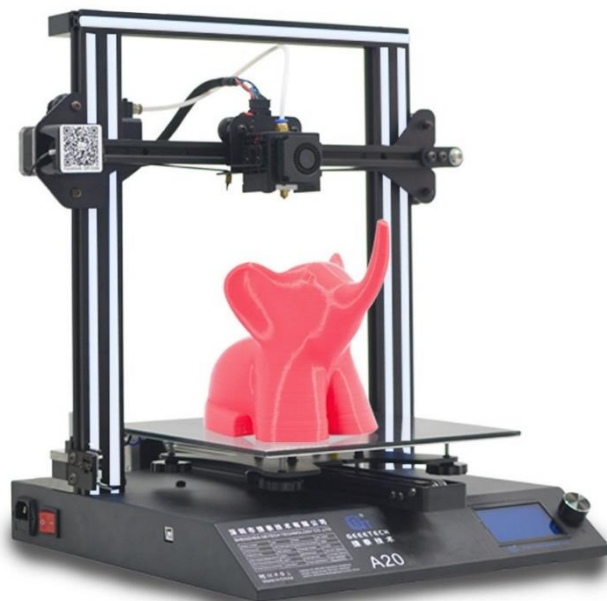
FDM принтер GIANTARM Nuova Geeetech A20 Stampante 3D , печать пластиком
